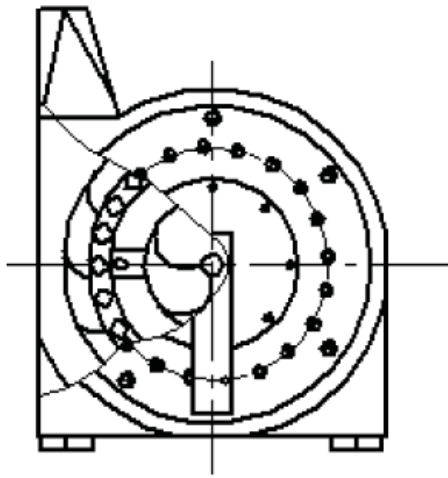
Конструкция дробилки зерна НИИСХ Северо-Востока
